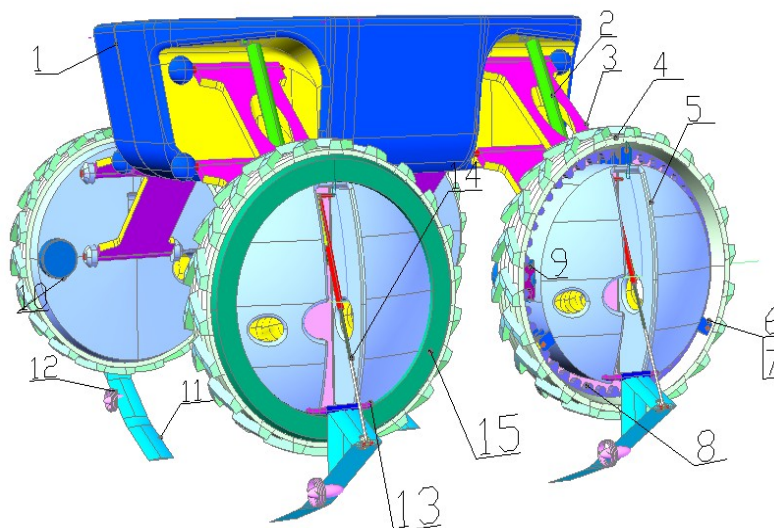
Амфибийное транспортное средство. 1 - корпус; 2 - амортизатор подвески колеса; 3 - тяга подвески колеса; 4 - обод; 5 - неподвижная втулка; 6 - стойки с осями; 7 - ролики; 8 - зубчатый венец обода; 9 - зубчатая шестерня; 10 - привод вращения обода; 11 - подводное крыло в выпущенном положении; 12 - гребной электропривод; 13 - ось вращения подводного крыла; 14 - линейный электропривод выпуска крыла; 15 - грязезащитный уплотняющий диск
